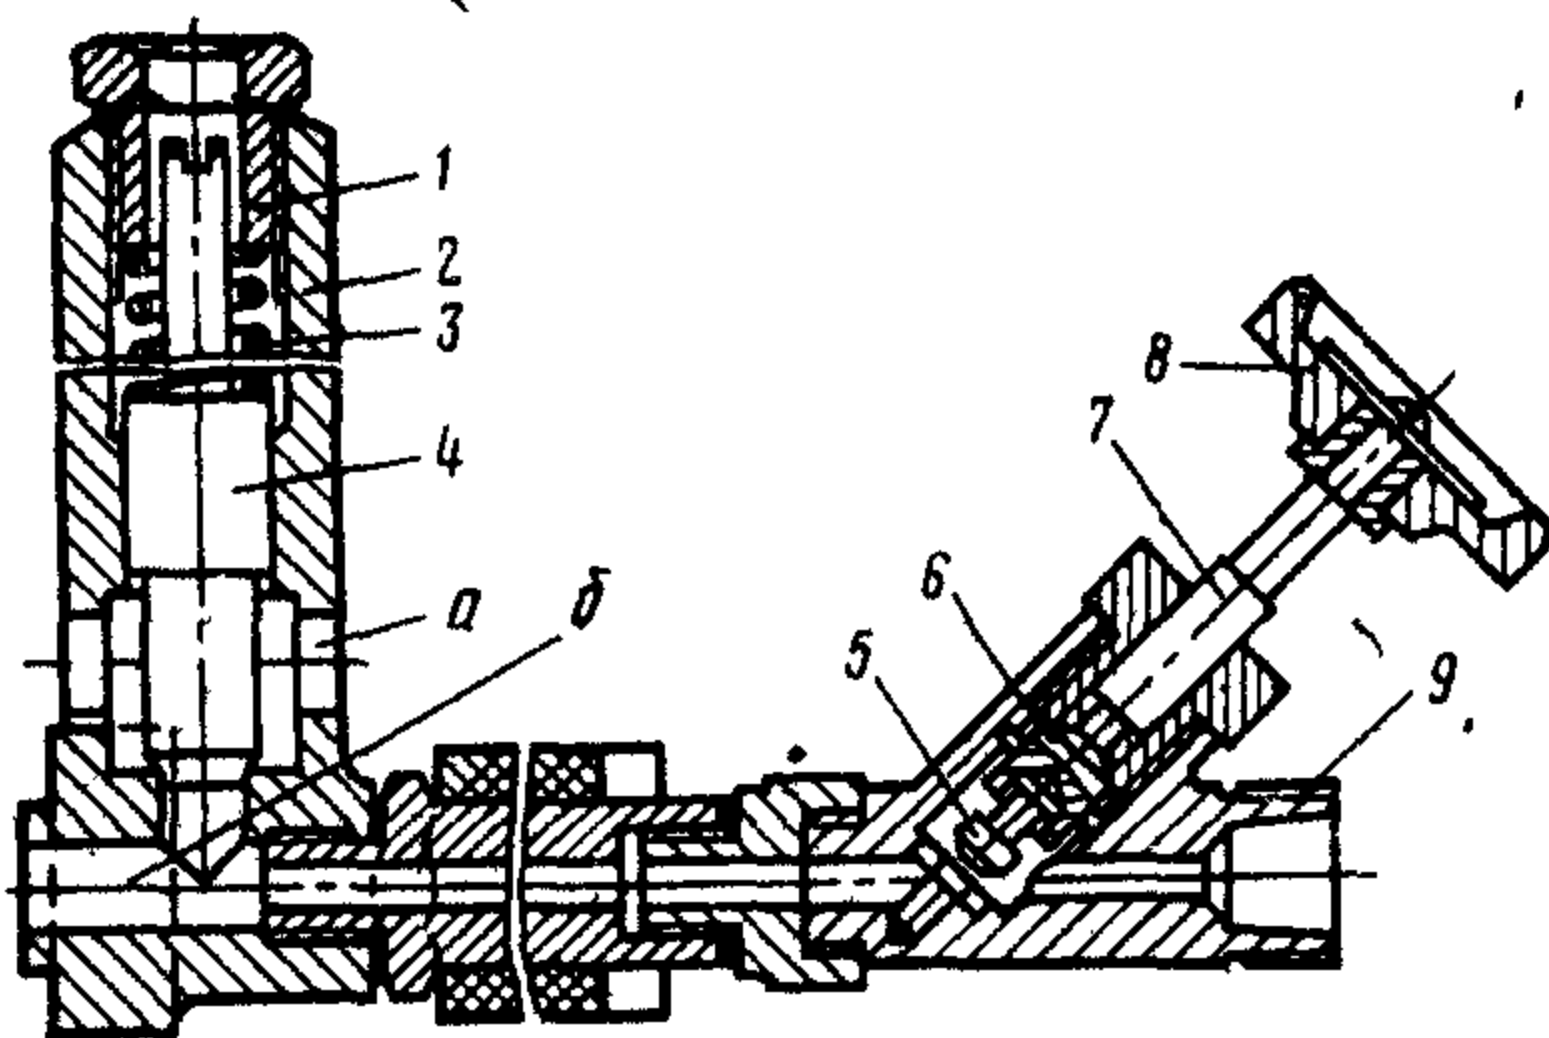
Предохранительный клапан и индикаторный кран двигателя Л275
